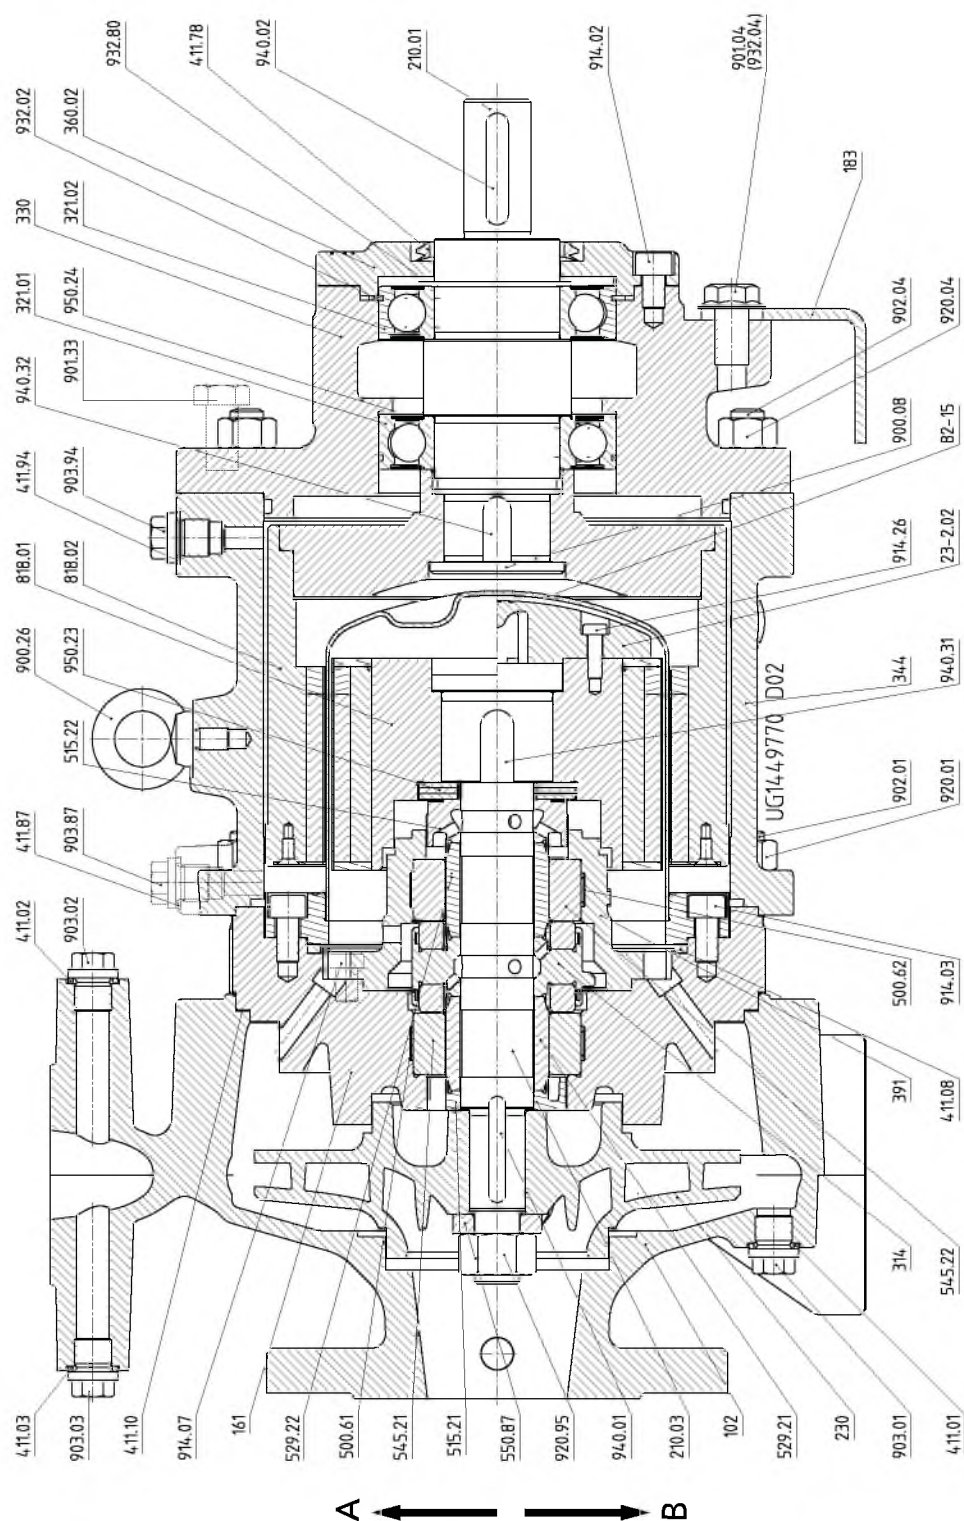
Сборочный чертеж — исполнение с зажимной крышкой без проставка
